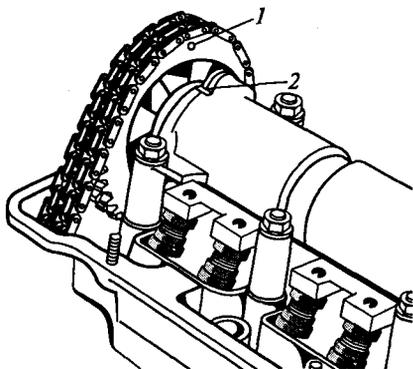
Положение установочных меток на звездочке распределительного вала и корпусе подшипников:
